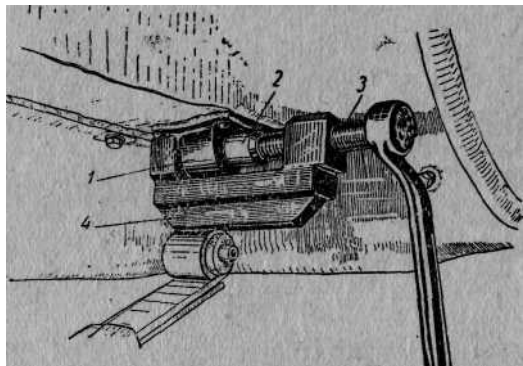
Запрессовка резино-металлического блока (втулки) в ушко коренного листа рессоры при помощи втулки-выколотки.
